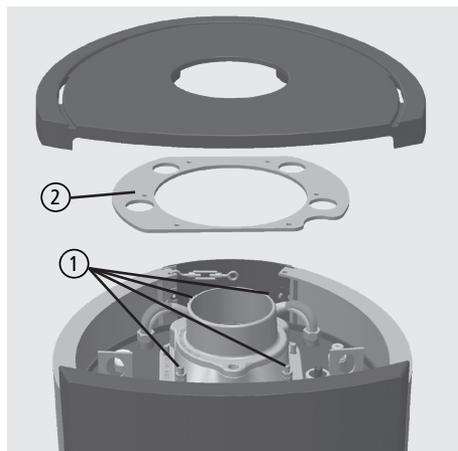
DELTA W: Points de pose du couvercle, plaque support
